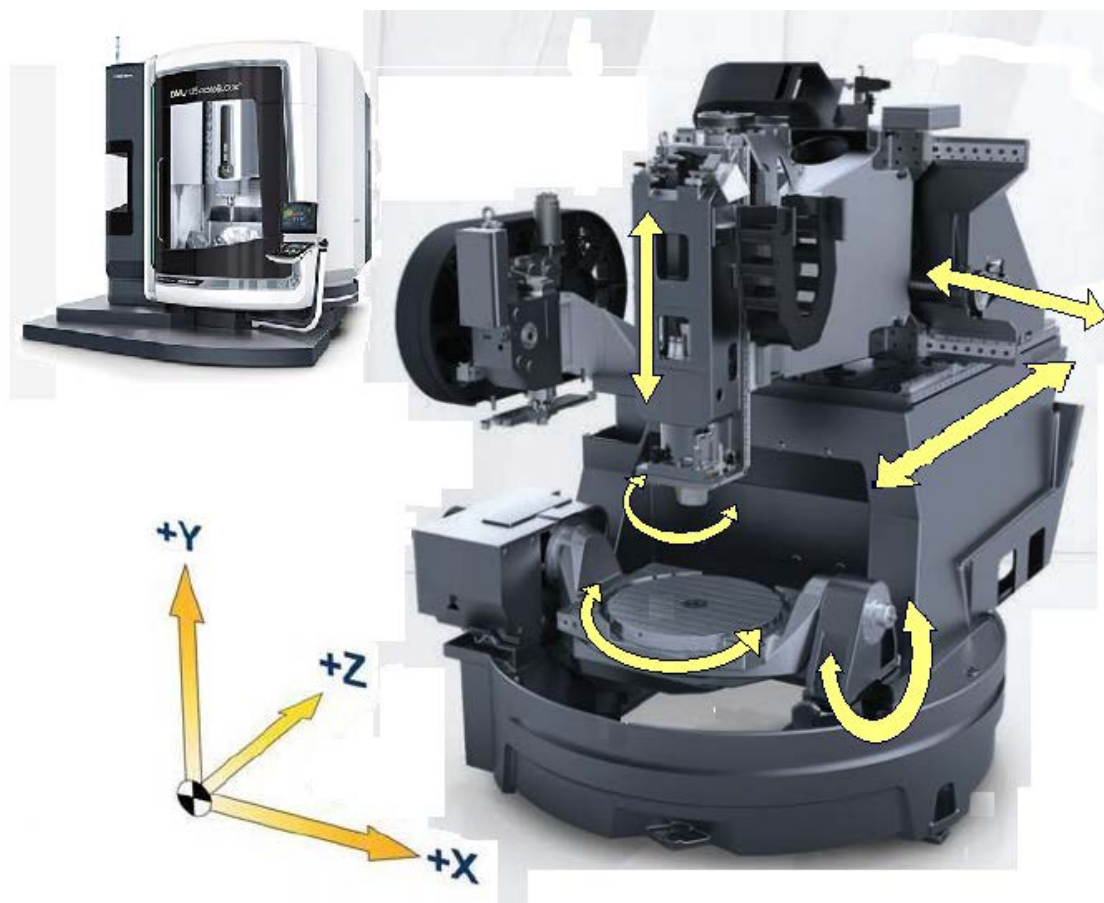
Универсальный фрезерный станок DMG DMU125
